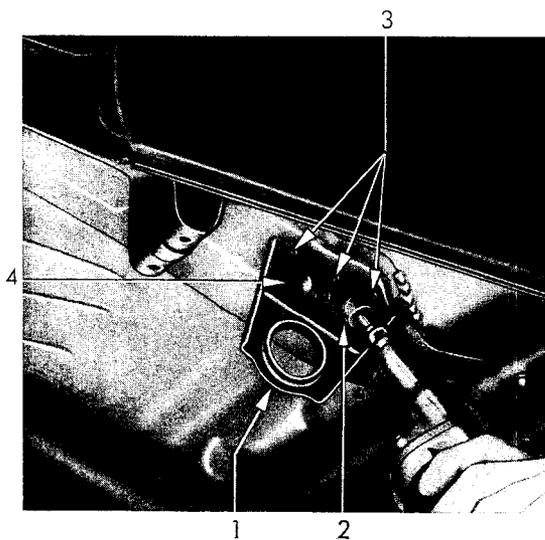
Warzenschweißpunkte an äußerer Stütze ausschleifen
